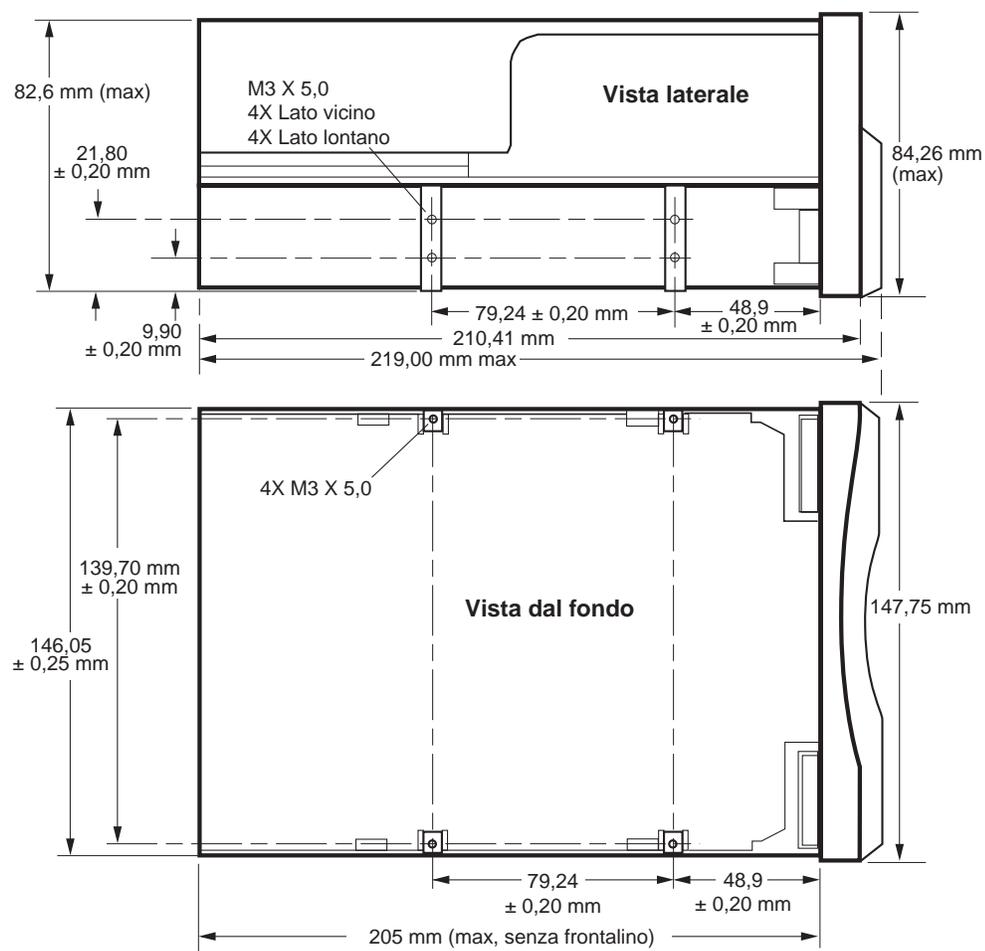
Drive Viper HVD/LVD interno — dimensioni
